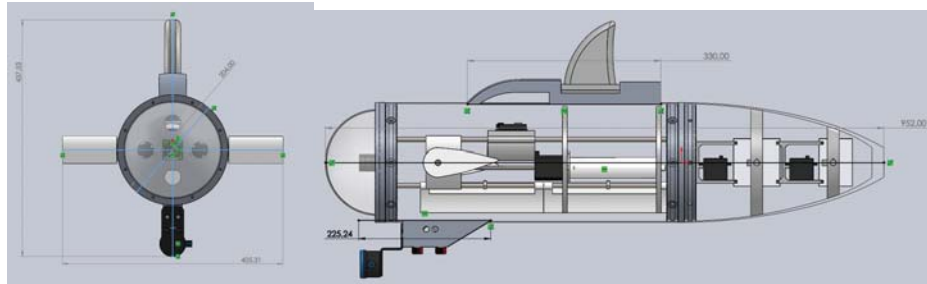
Dimensões do Protótipo V3 - Vista Frontal (Esquerda) e Lateral (Direita)
